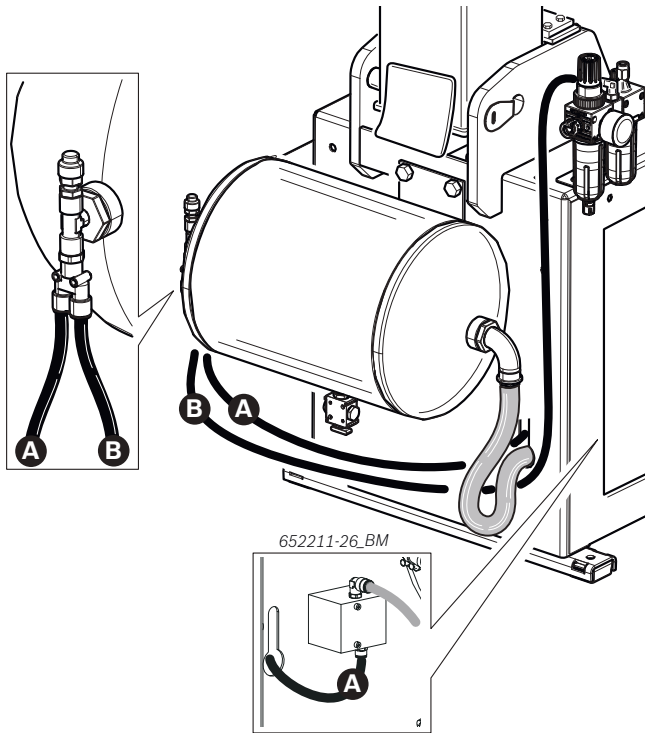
Druckluftanschlüsse für Druckluftbehälter
